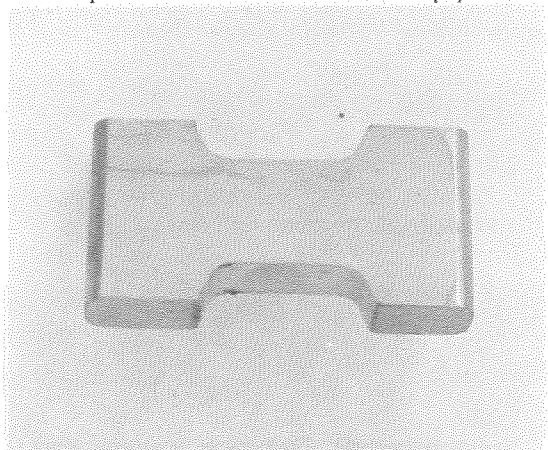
Grietas previas al ensayo de tracción de probetas compactadas con punzones conformantes.
